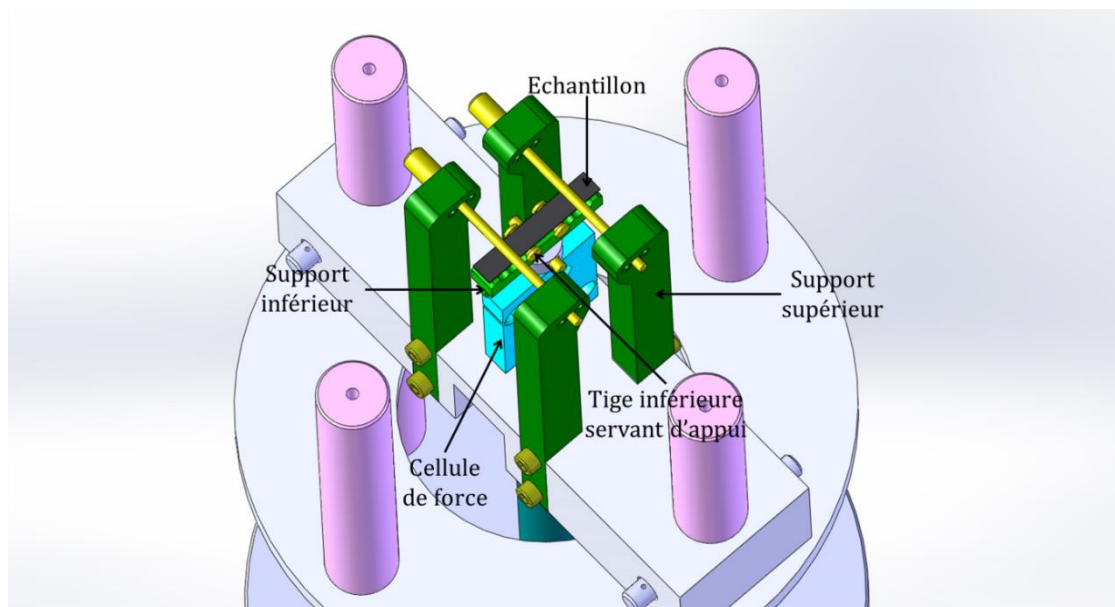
Dessin CAO de la machine de flexion quatre-points : vue 3D détaillée de la partie supérieure.
